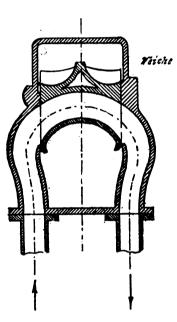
Apparat mit eingebauter Weiche auf Durchgang gestellt.
